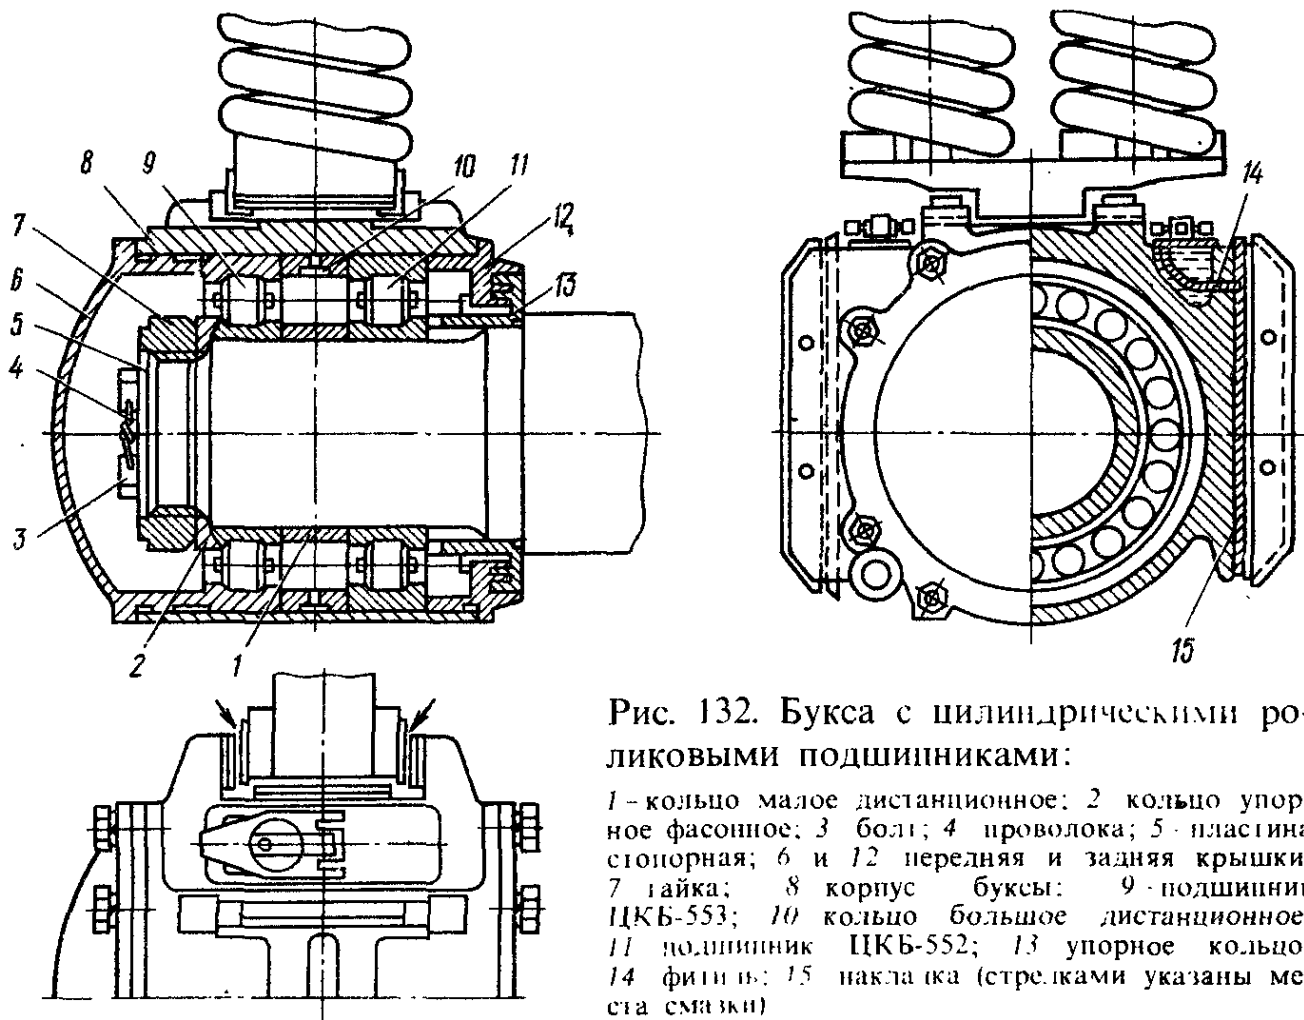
Букса с цилиндрическими роликовыми подшипниками:
